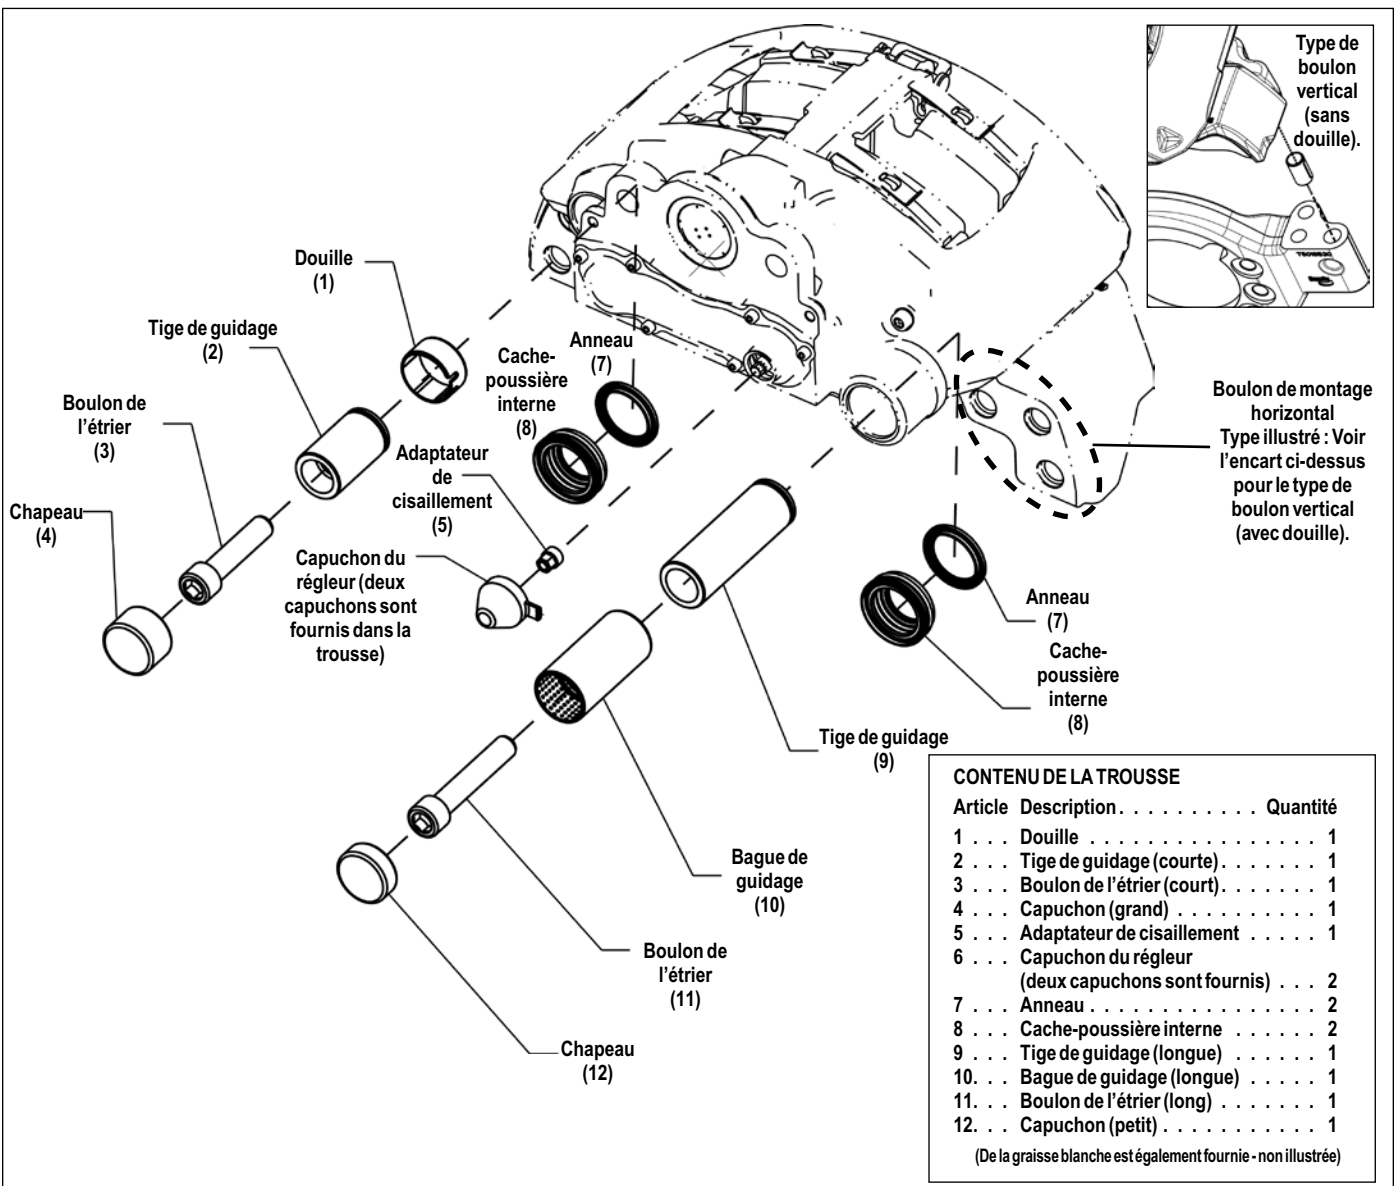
VUE EXPLOSÉE DE LA TIGE DE GUIDAGE
